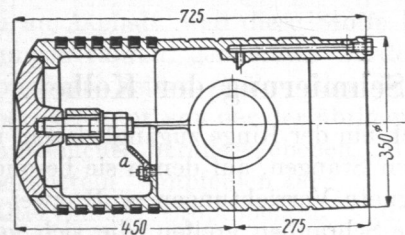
Gasmaschinenkolben mit besonders eingesetztem Boden.
